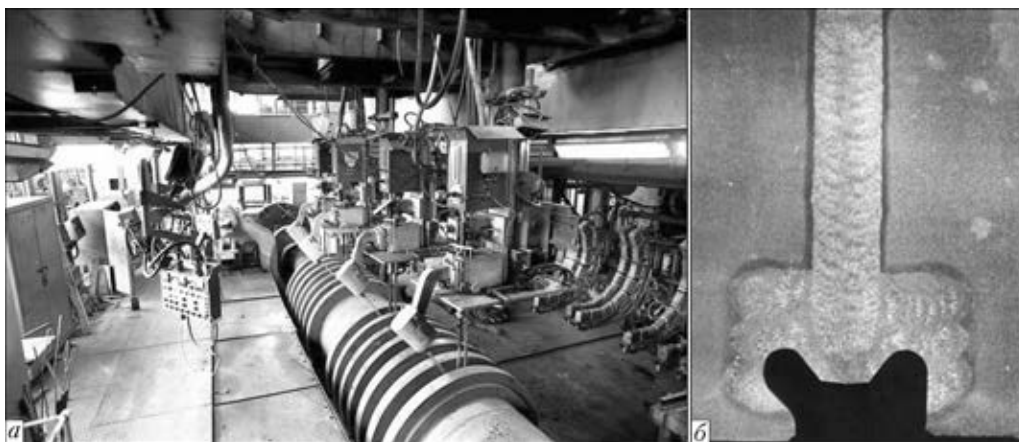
Автоматическая сварка под флюсом ротора паровой турбины мощностью 1000 МВт для АЭС (а) и макрошлиф металла сварного шва ротора паровой турбины (б)
